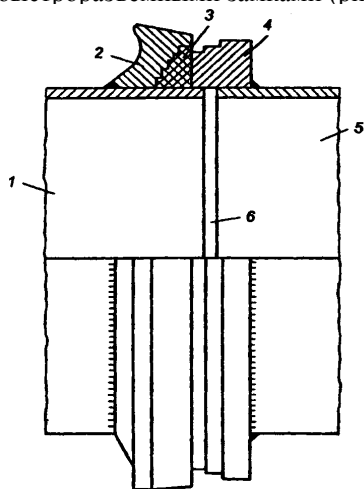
Фланцевое соединение двух звеньев: 1, 5 – звенья; 2 – фланец с кольцевым пазом; 3 – уплотнительное резиновое кольцо; 4 – фланец с кольцевым гребнем; 6 – кольцевой зазор.
